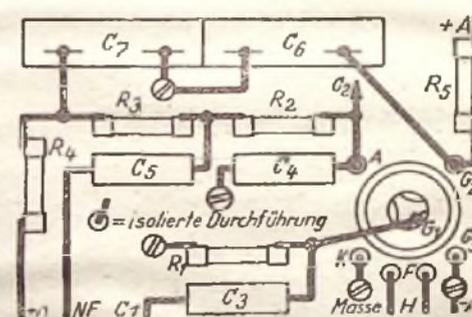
Verdrahtungsplan einer Audionstufe mit RV 12 P 2000
